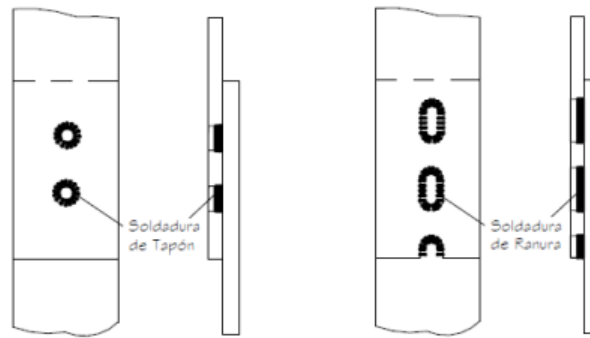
Soldadura tipo tapón y muesca. Fuente: Rodríguez (2016).
